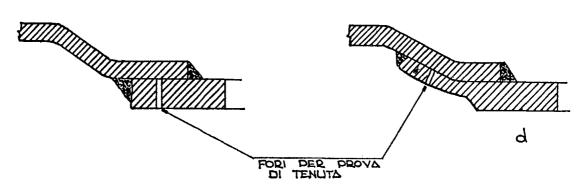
Saldature di pozzetti per involucri con λ = 0,8
